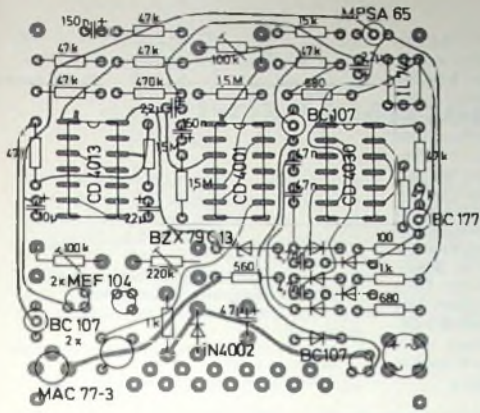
Bestückungsplan der Printplatte für die elektronisch gesteuerte Überblendprojektion
